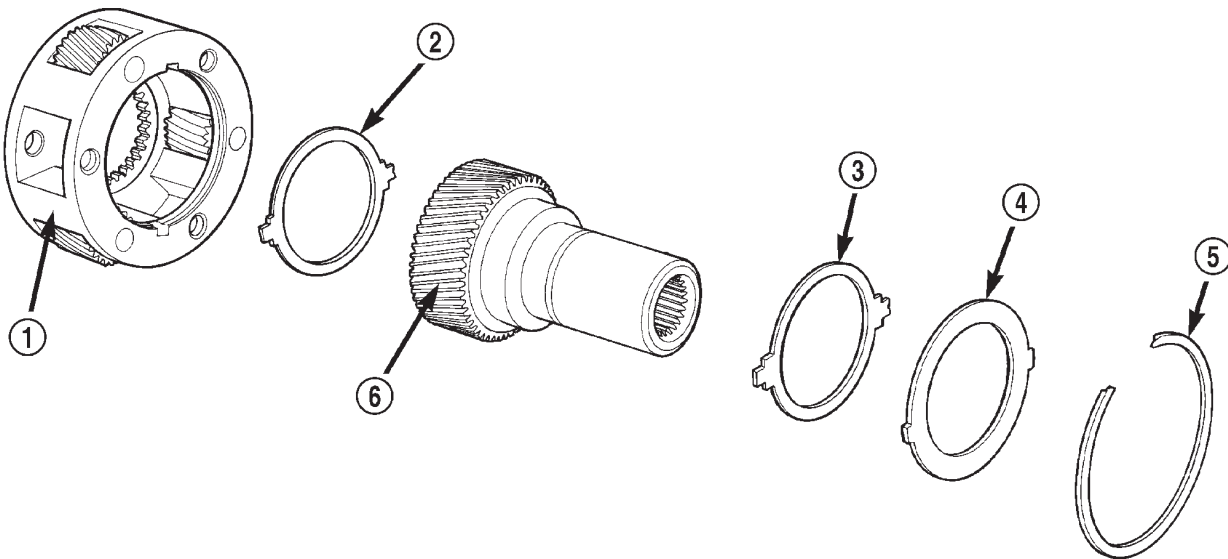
Componentes del engranaje impulsor y caja de satélites
